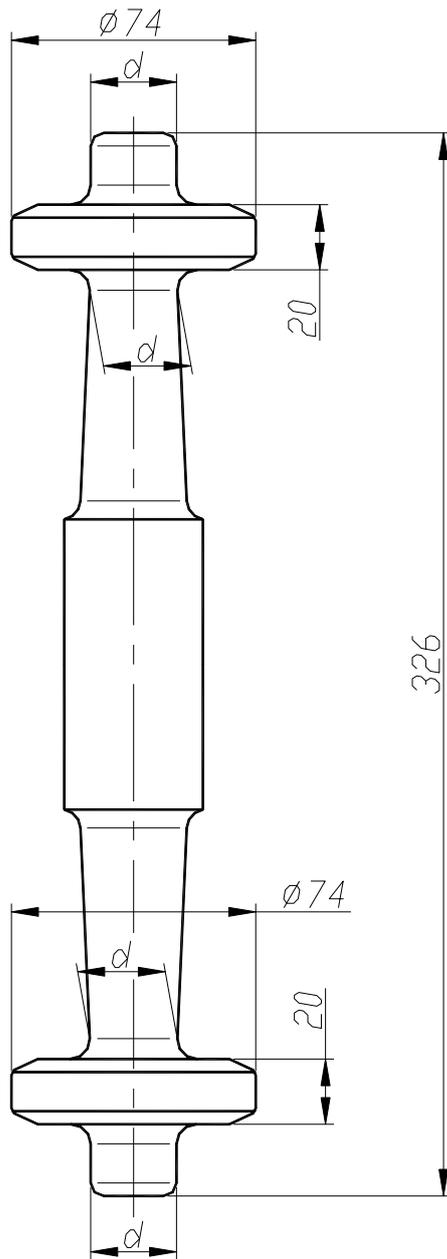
Опора редуктора ЕЮК-160-1М и ВБА-32/2
